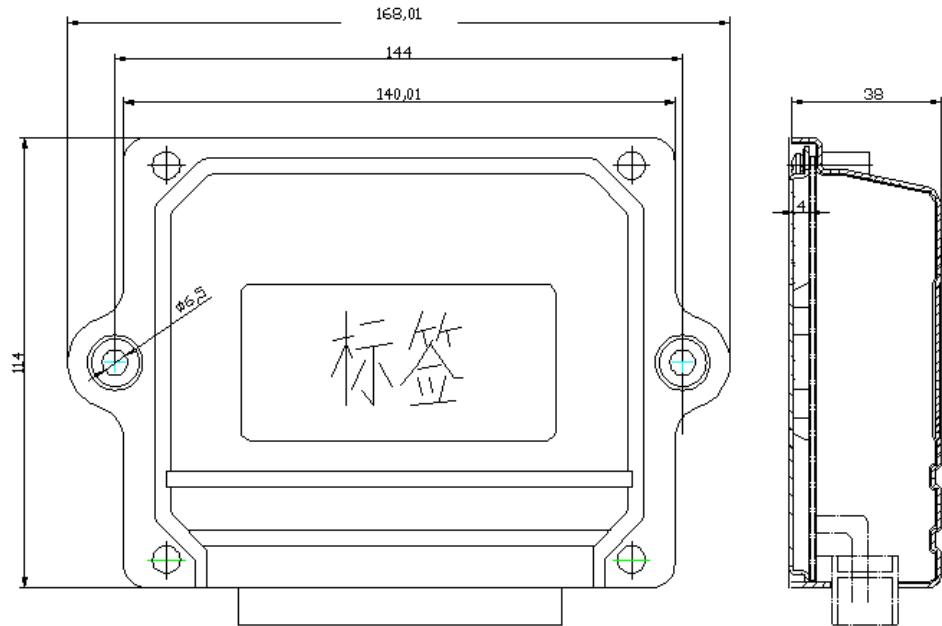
DK202,DK102 安装尺寸/Fig.6-2-2 Installing Dimension of DK202 and DK102
